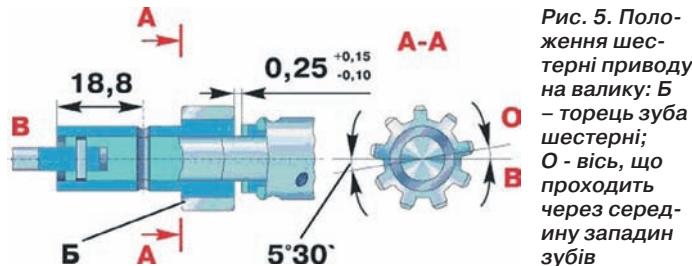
Положення шестерні приводу на валику: Б – торець зуба шестерні; О – вісь, що проходить через середину западин зубів
